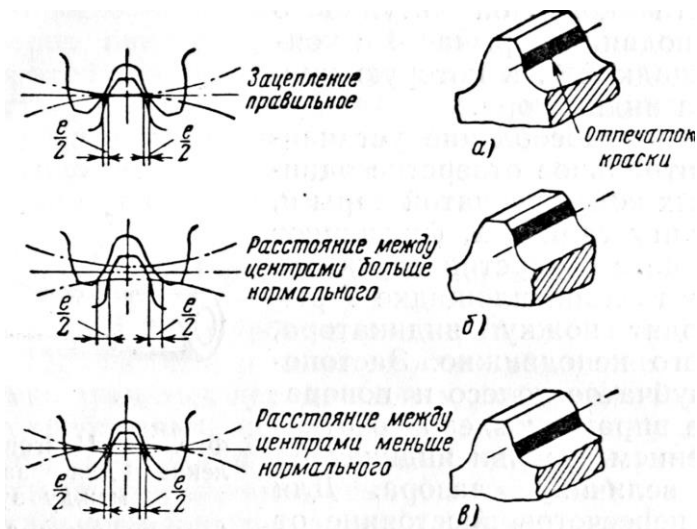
Качество зацепления цилиндрических зубчатых колес, определяемое по отпечатку
